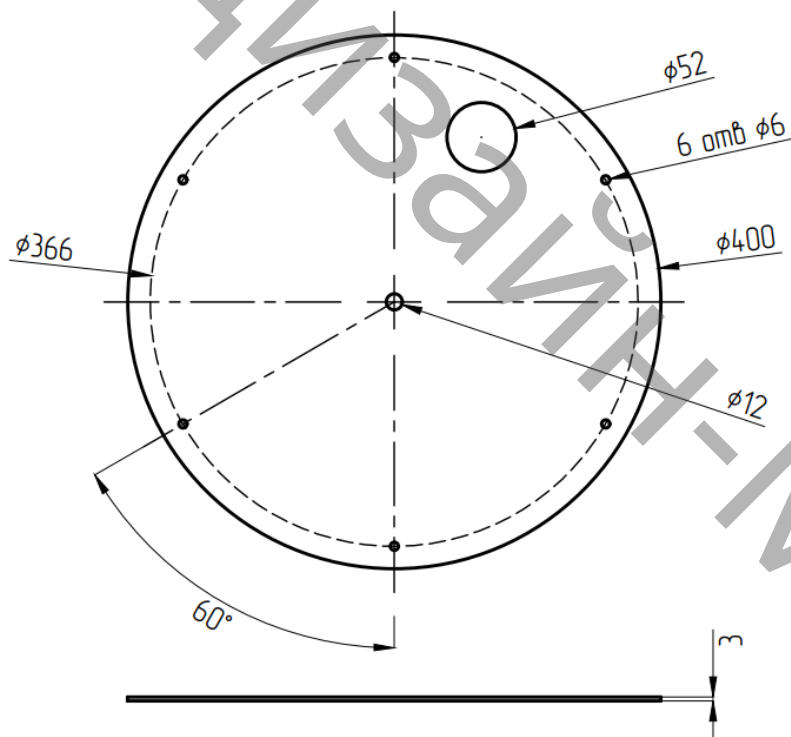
общий вид стандартной крышки верхней секции ФК30.
